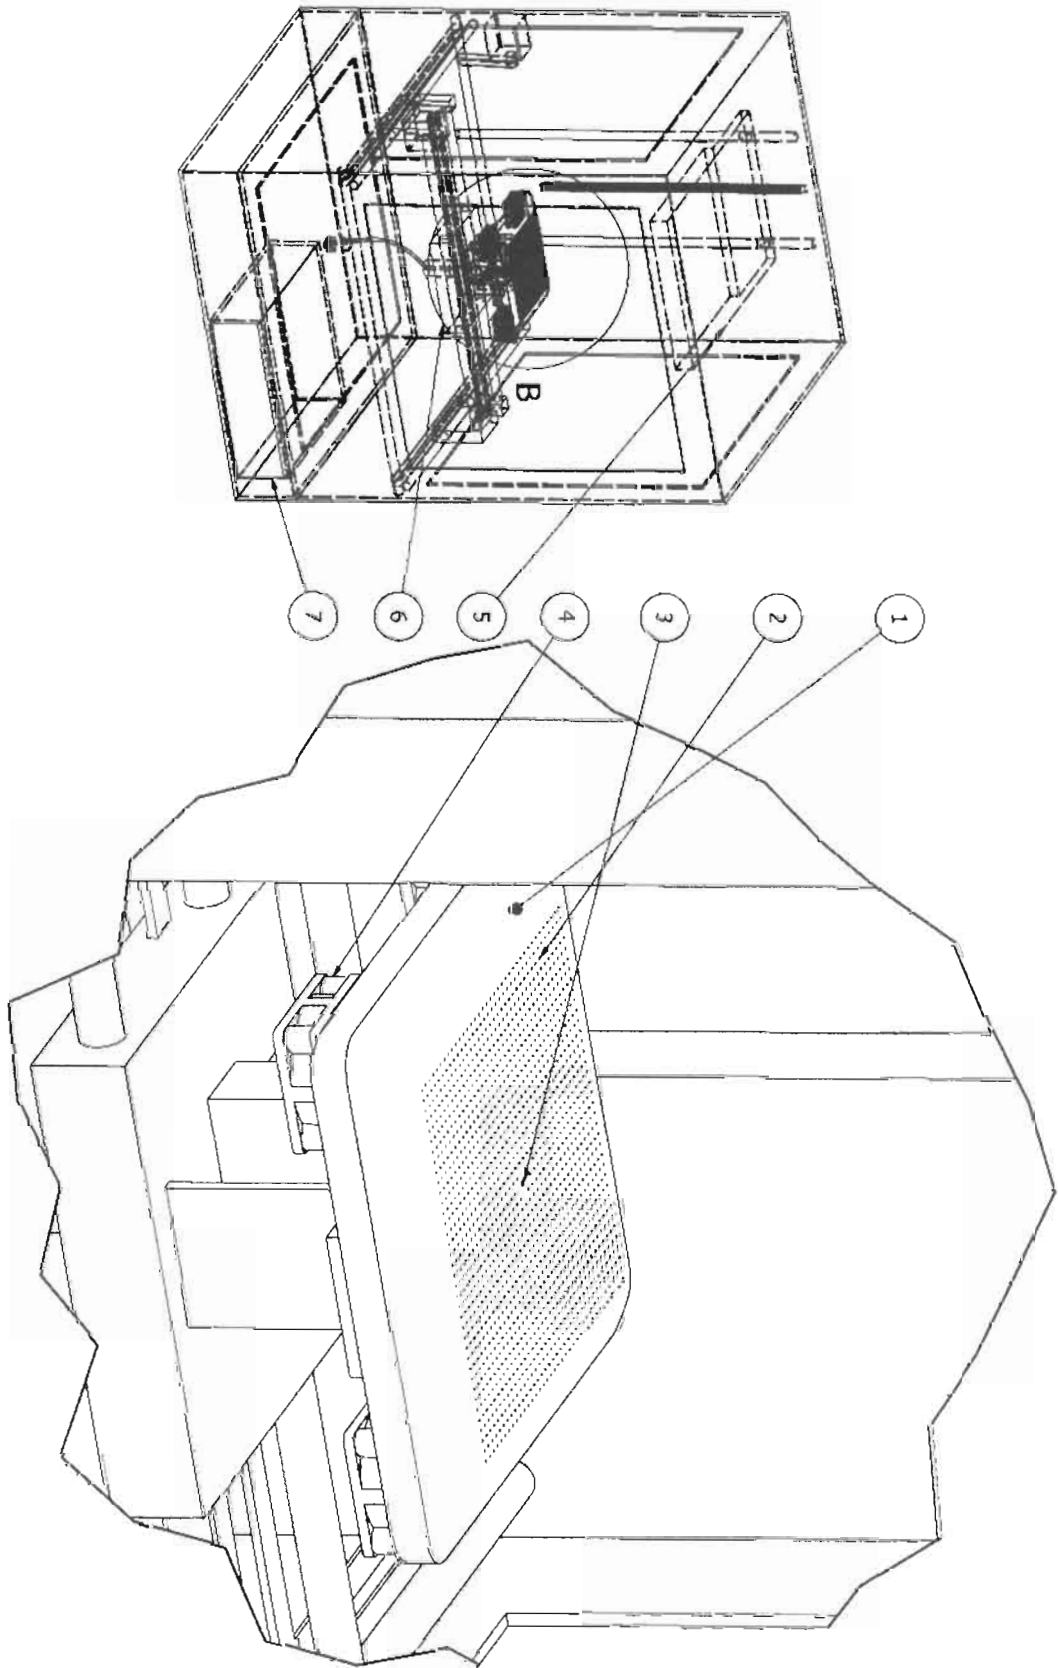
Axonometria imprimantei 3D cu support fizic solidar cu duza de extrudare.
